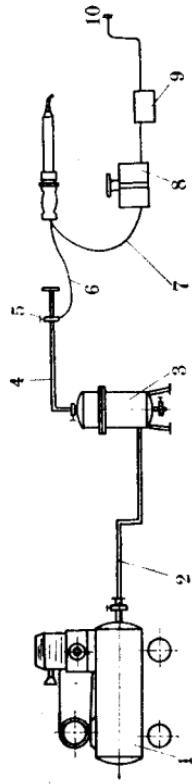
硬聚氯乙烯塑料的焊接设备及配置
